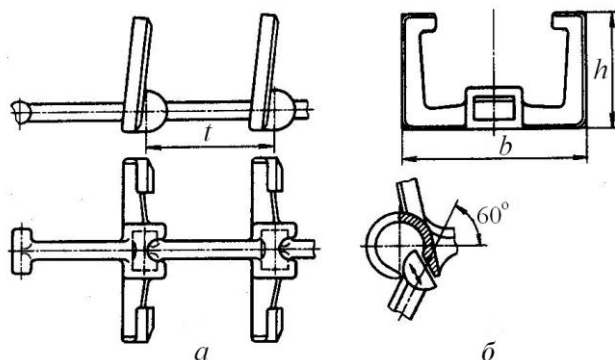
Литая разборная цепь из ковкого чугуна: *a* – конструкция; *б* – способ сборки-разборки
